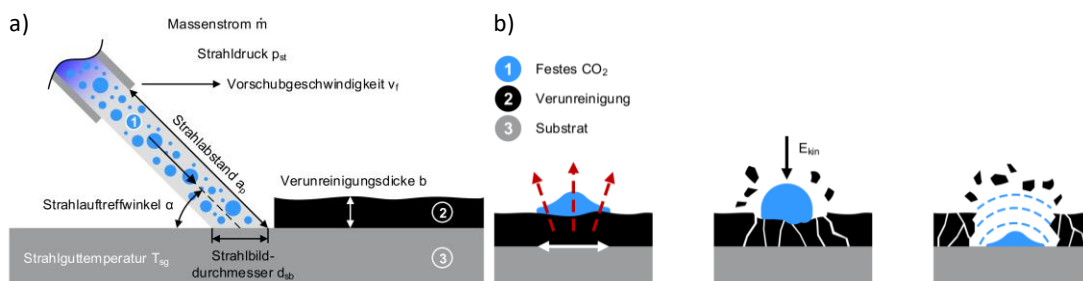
Strahlen mit festem Kohlendioxid: a) Einstellparameter; b) Wirkmechanismen
